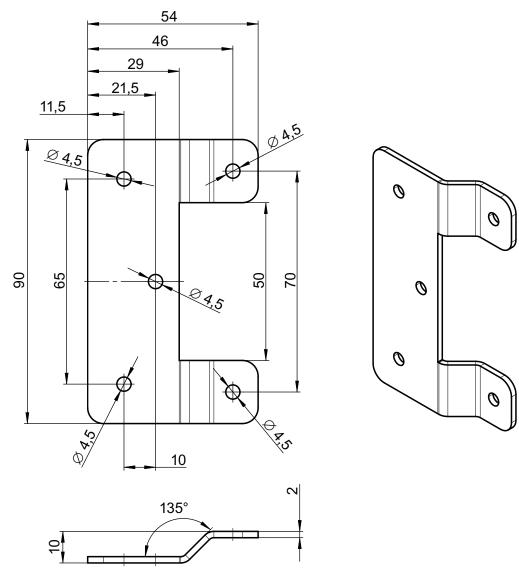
Montaje mural de X-300EEC (medidas en mm)
